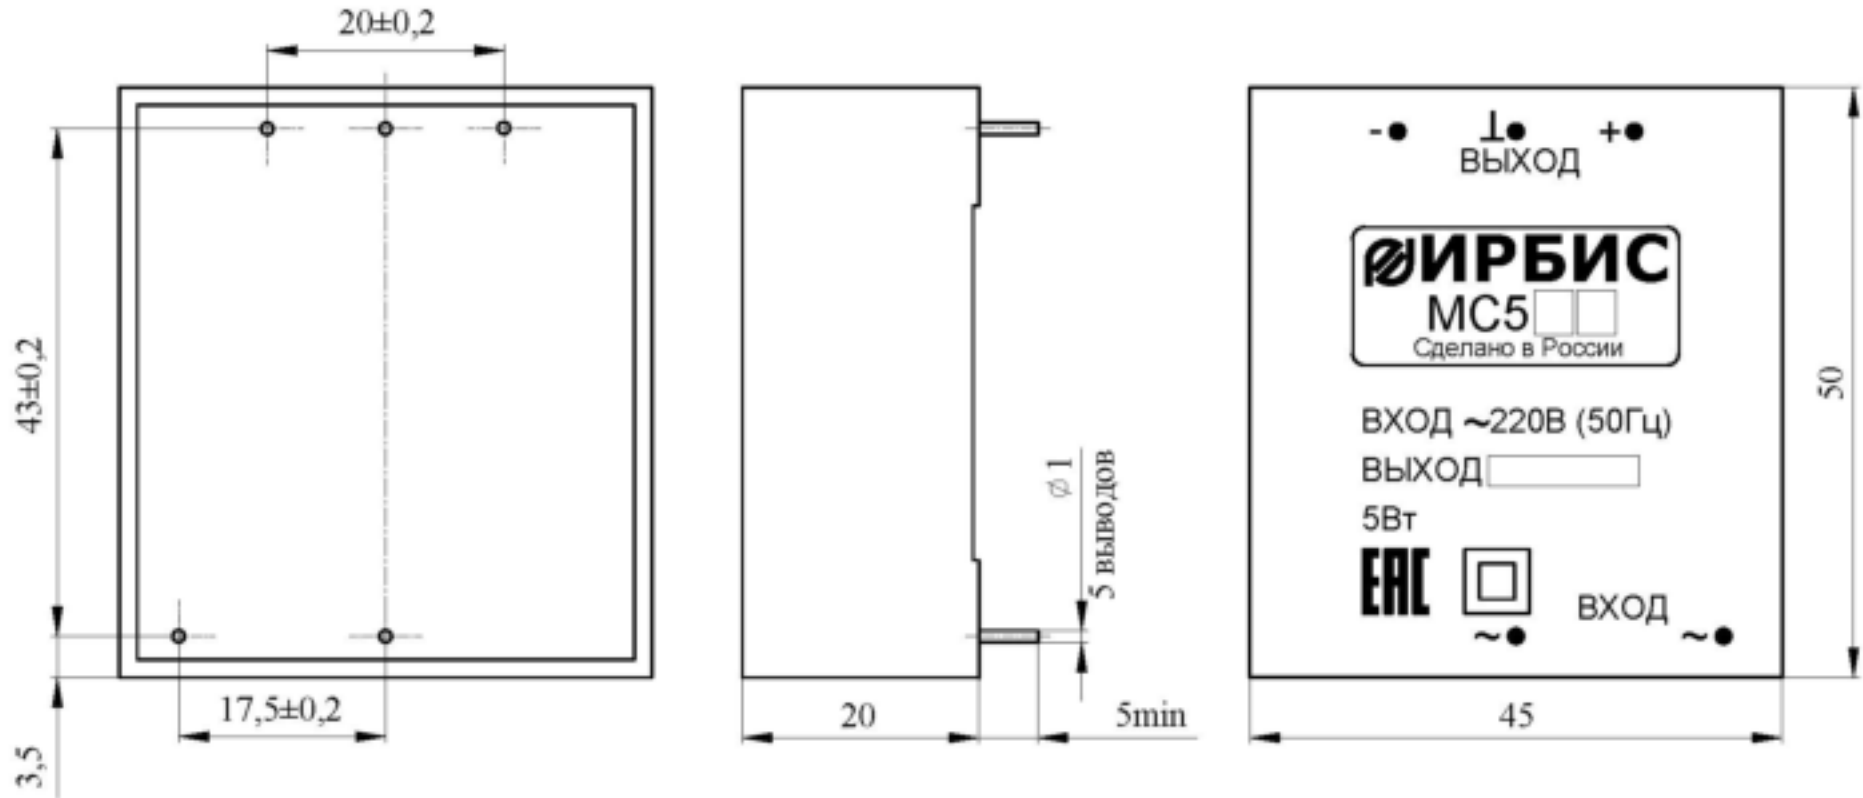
Габаритный чертеж модулей серии MC5\_2к
